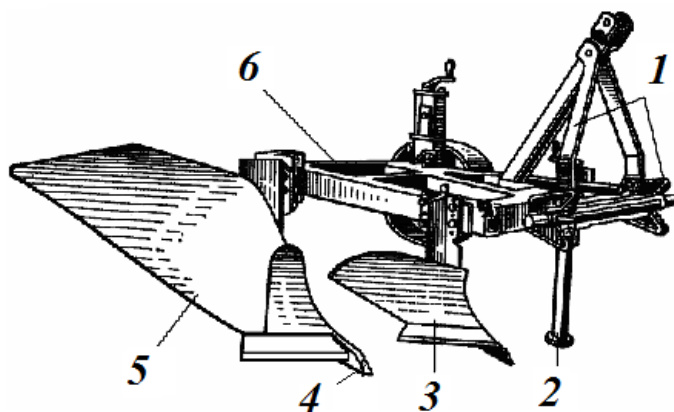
Плуг плантажний начіпний ППН-50: 1 - автоматичний начіпний пристрій; 2 - підніжка; 3 - передплужник; 4 - долото; 5 - основний корпус; 6 - рама
